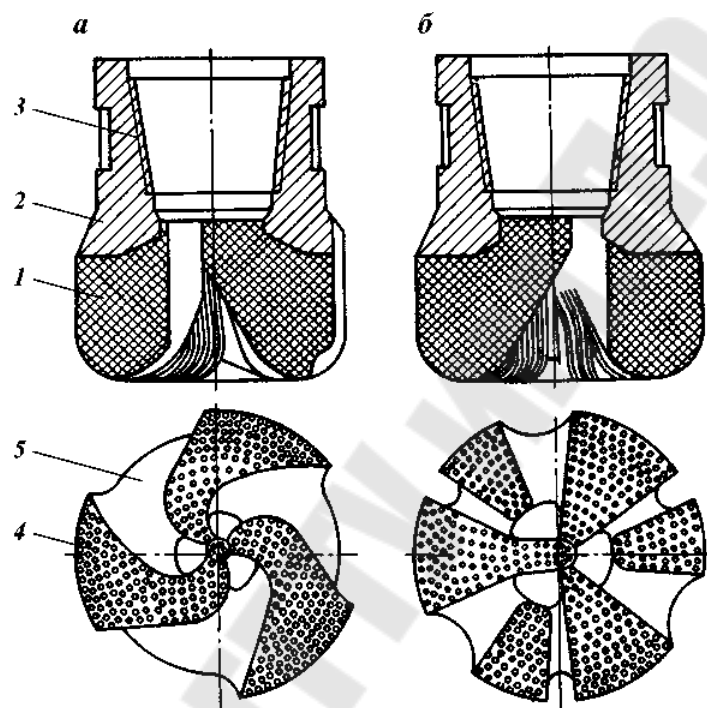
Конструкция алмазного долота для бурения сплошным забоем: а, б - разные конструкции рабочих элементов: 1 – твердосплавная алмазо- несущая матрица; 2 – стальной корпус долота; 3 - замковая резьба; 4 - контактный сектор; 5 - выемка для циркуляции промывочного агента
